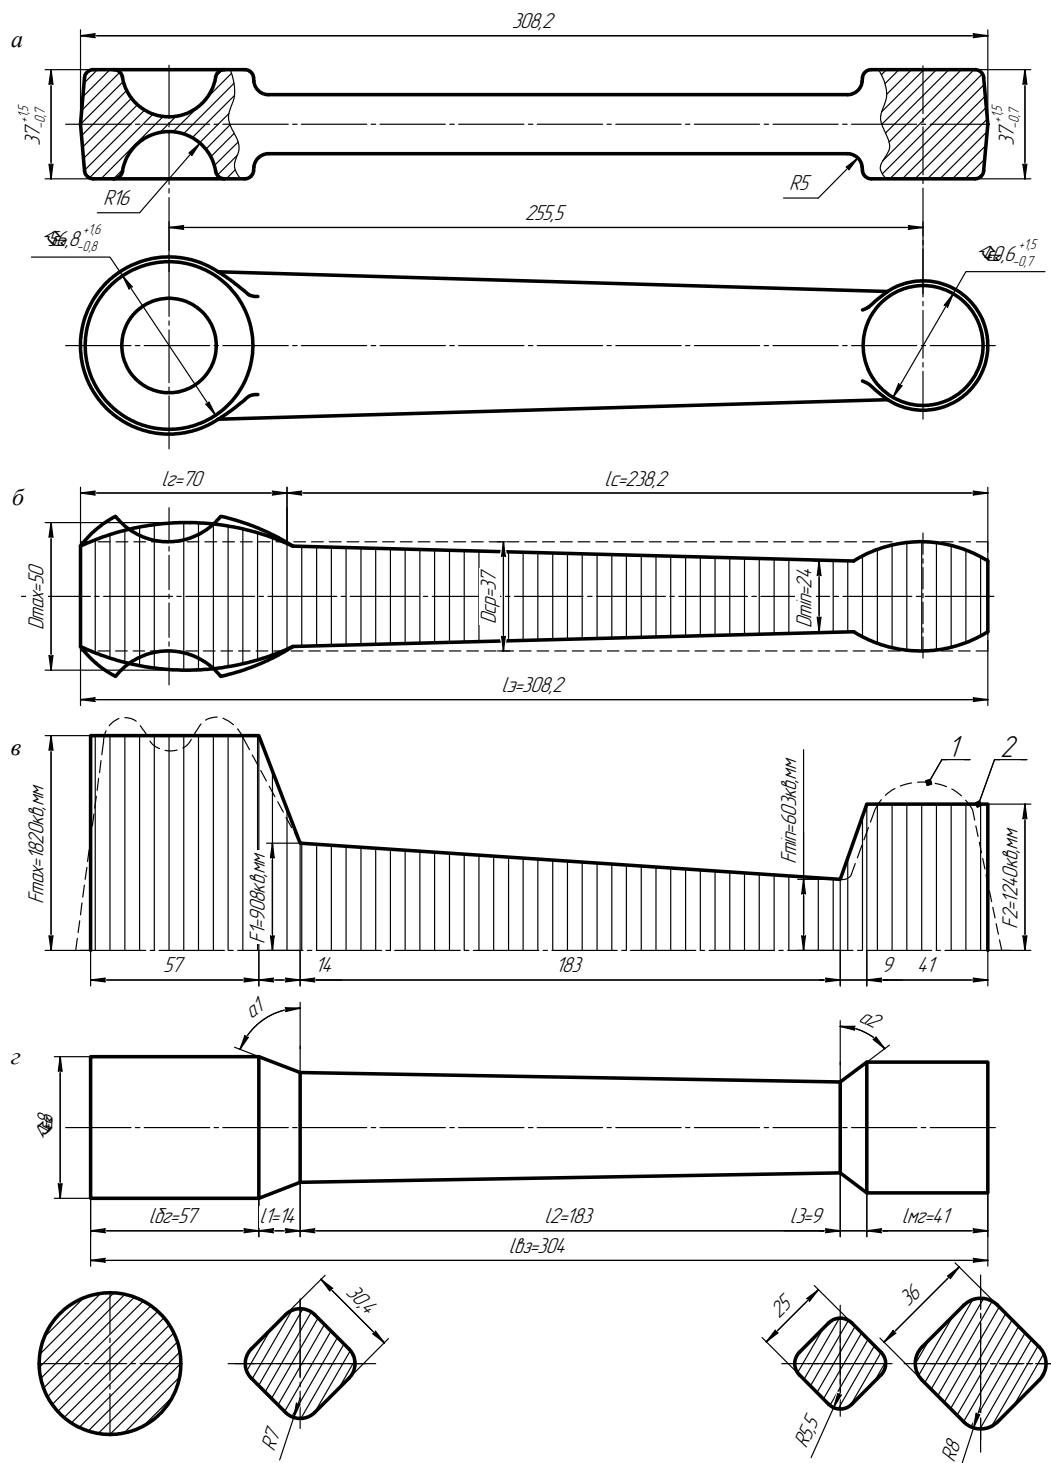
Конструирование вальцованной заготовки для поковки рычага:
